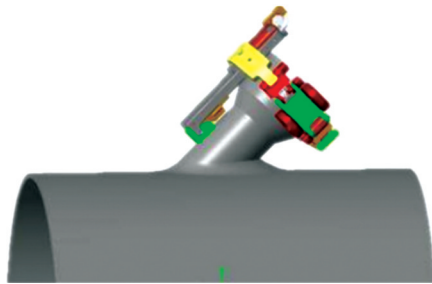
BOSS头焊缝及堆焊层 PAUT 检验示意
